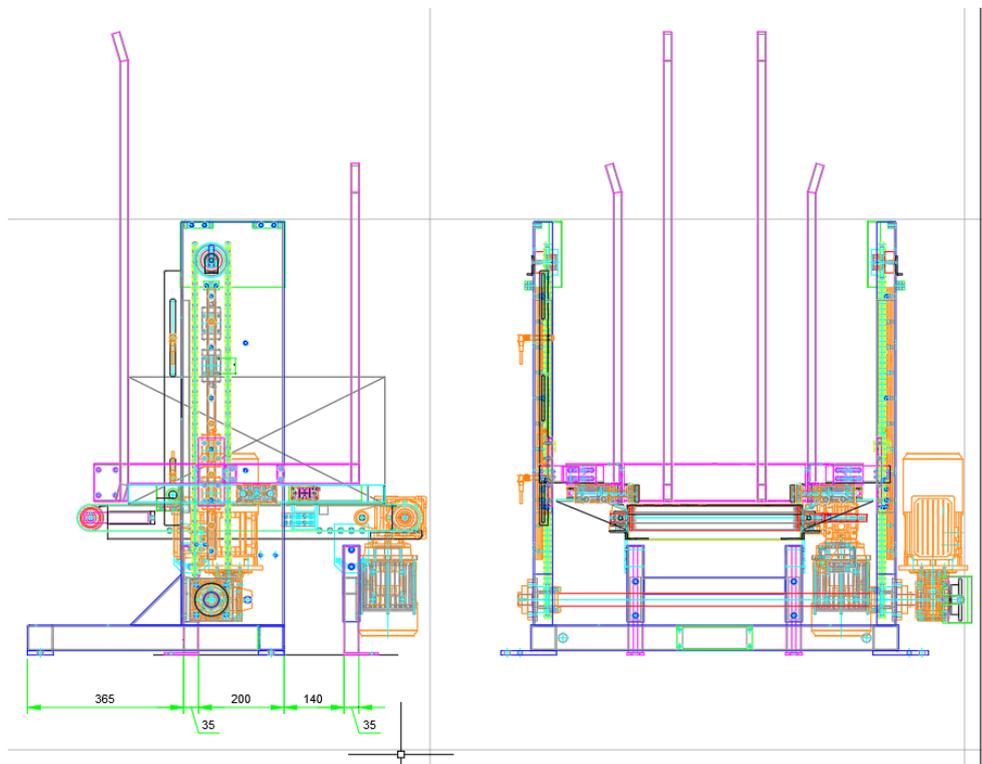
, vistas de alzado y perfil del desapilador de cajas ya existente en la empresa.
